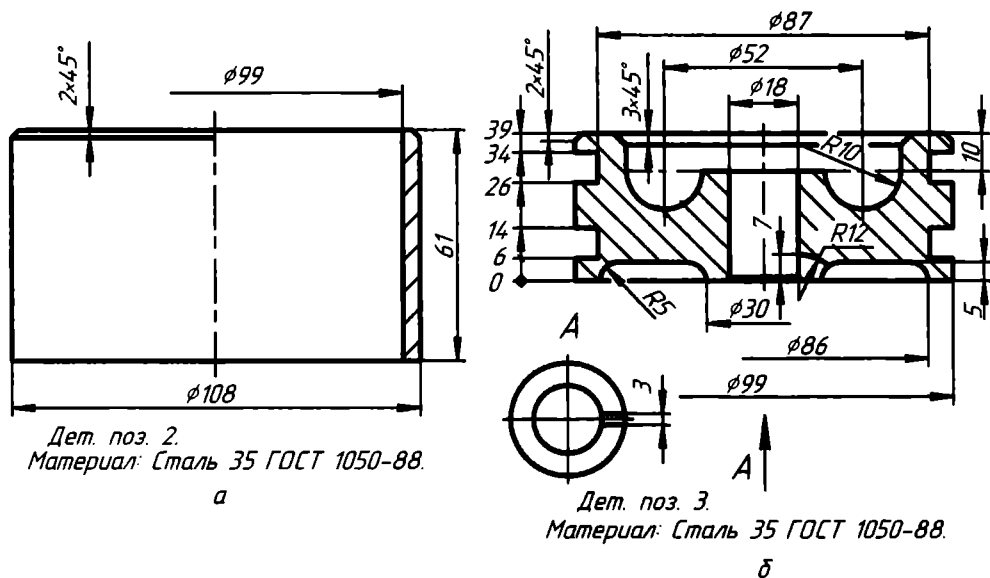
Чертежи: а — гильзы; б — поршня
